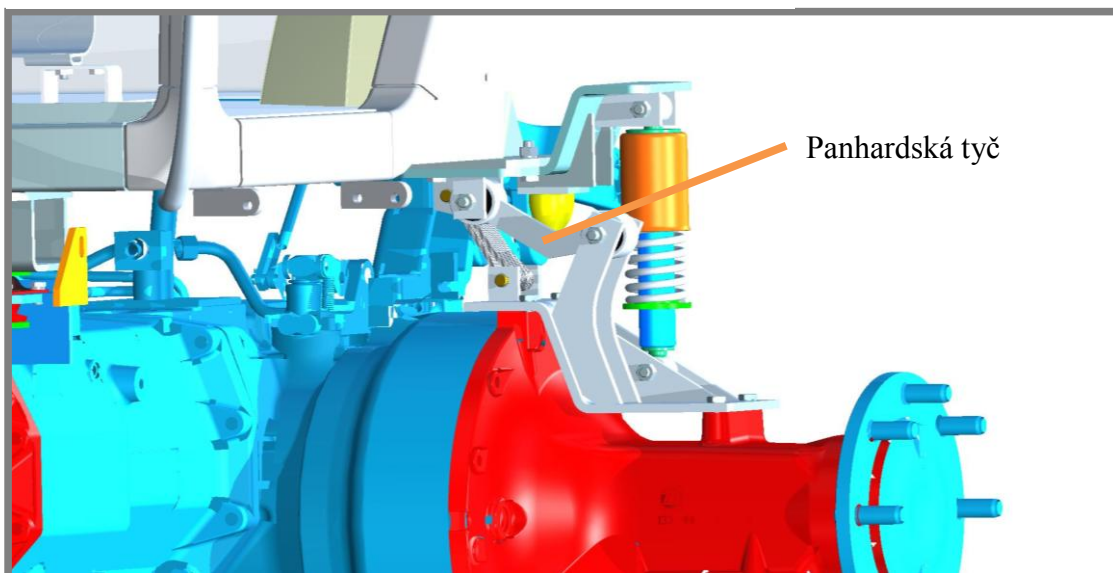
Konstrukční varianta 3, vertikální dorazy [18]
